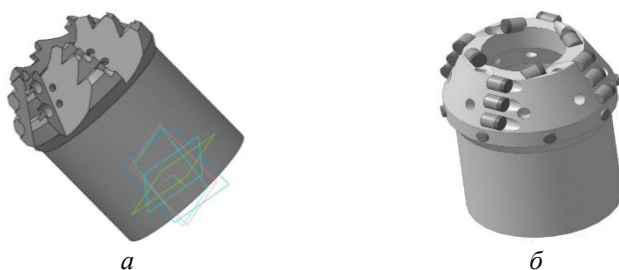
ПДС фиксированными резцами на ступенчатом корпусе бурголовок 106/47,6 мм: а – металлический ступенчатый корпус с промысловыми отверстиями, б – корпус оснащенный ПДС резцами
